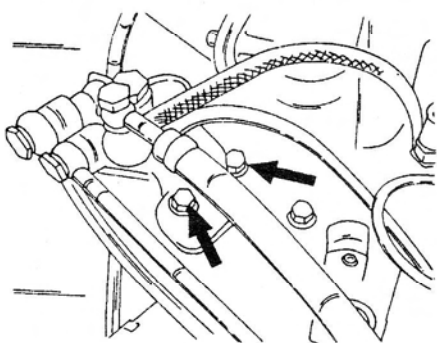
Топливный фильтр крепится к двигателю двумя болтами (стрелки).
